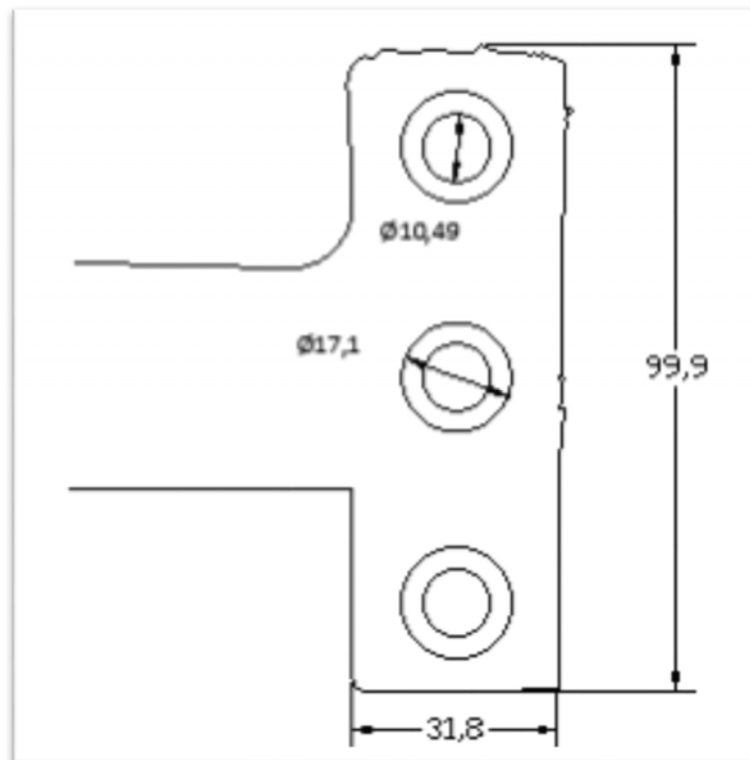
Sección longitudinal de pieza soldada (Fotogrametría)
